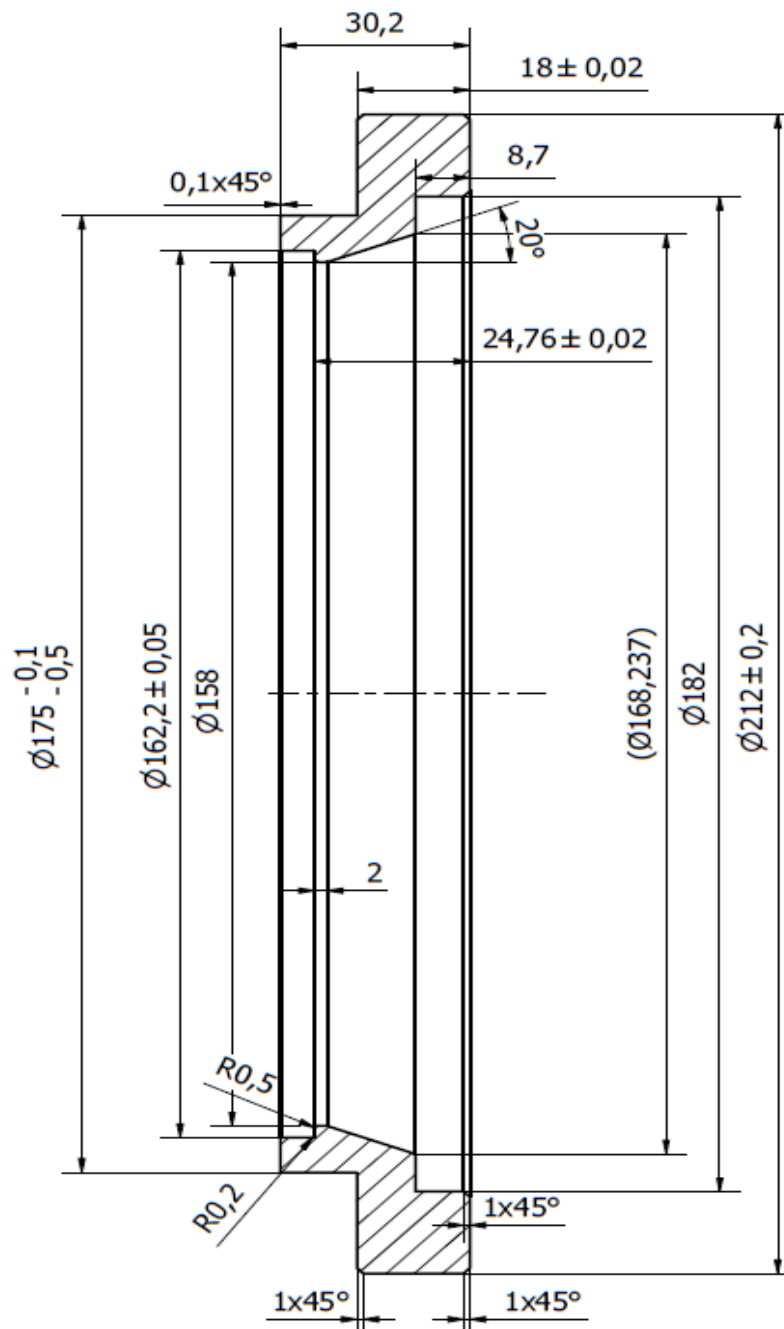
Stahovací pouzdro Hardinge 25C Collet 65MM [50]
